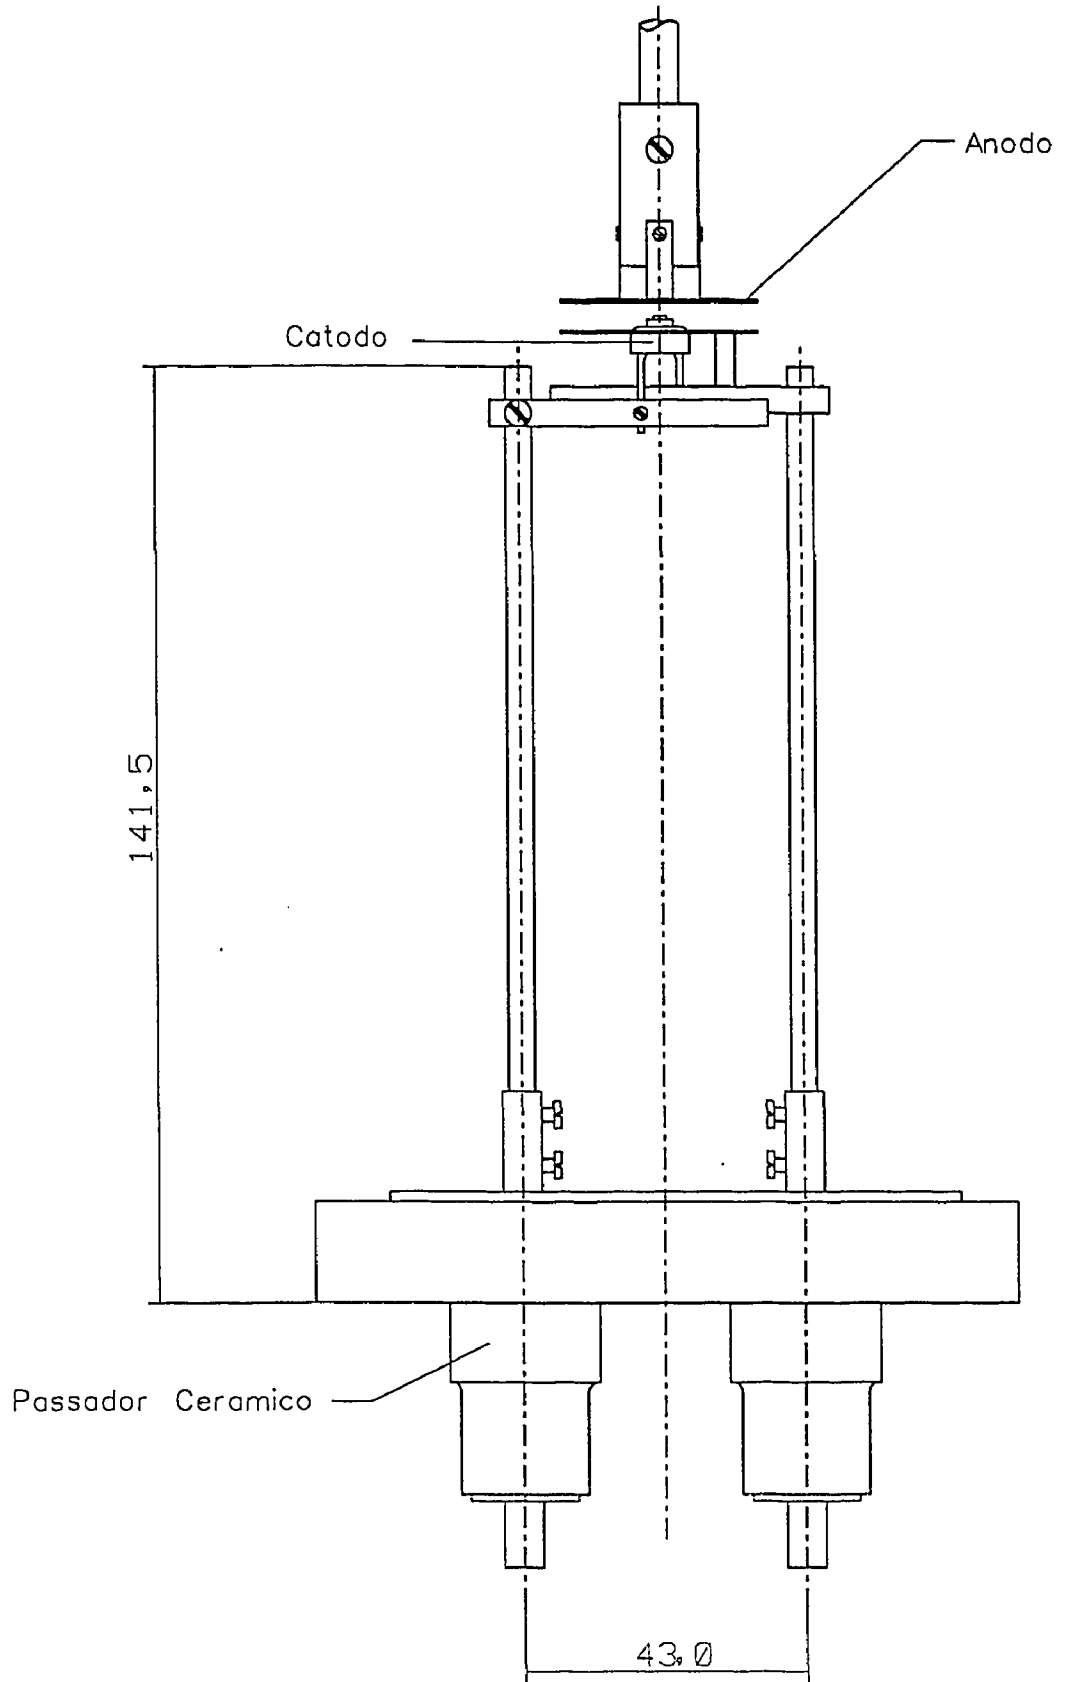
CONJUNTO TESTADOR DE CATODOS (dimensões em mm)
